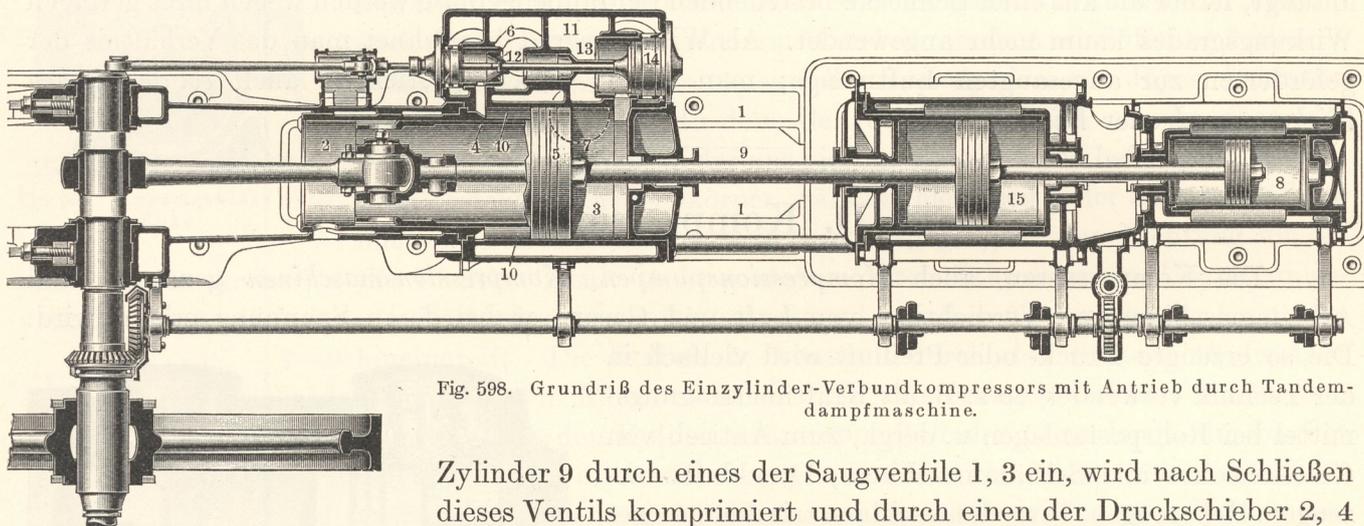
Grundriß des Einzylinder-Verbundkompressors mit Antrieb durch Tandemdampfmaschine.
